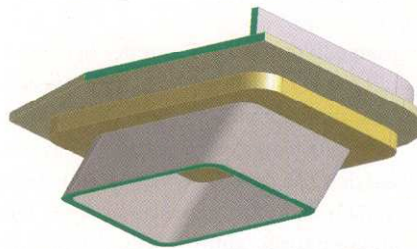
Zugeschnittenes Submodell mit den grün markierten Schnittflächen.
